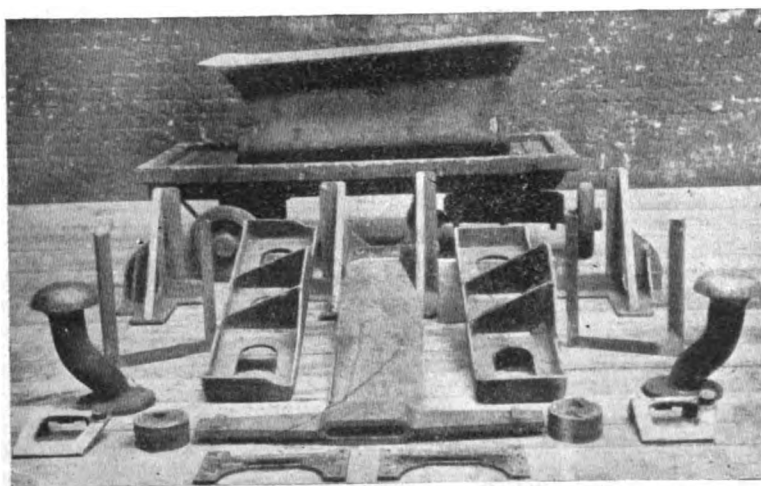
Saldatura elettrica di parti della locomotiva.
